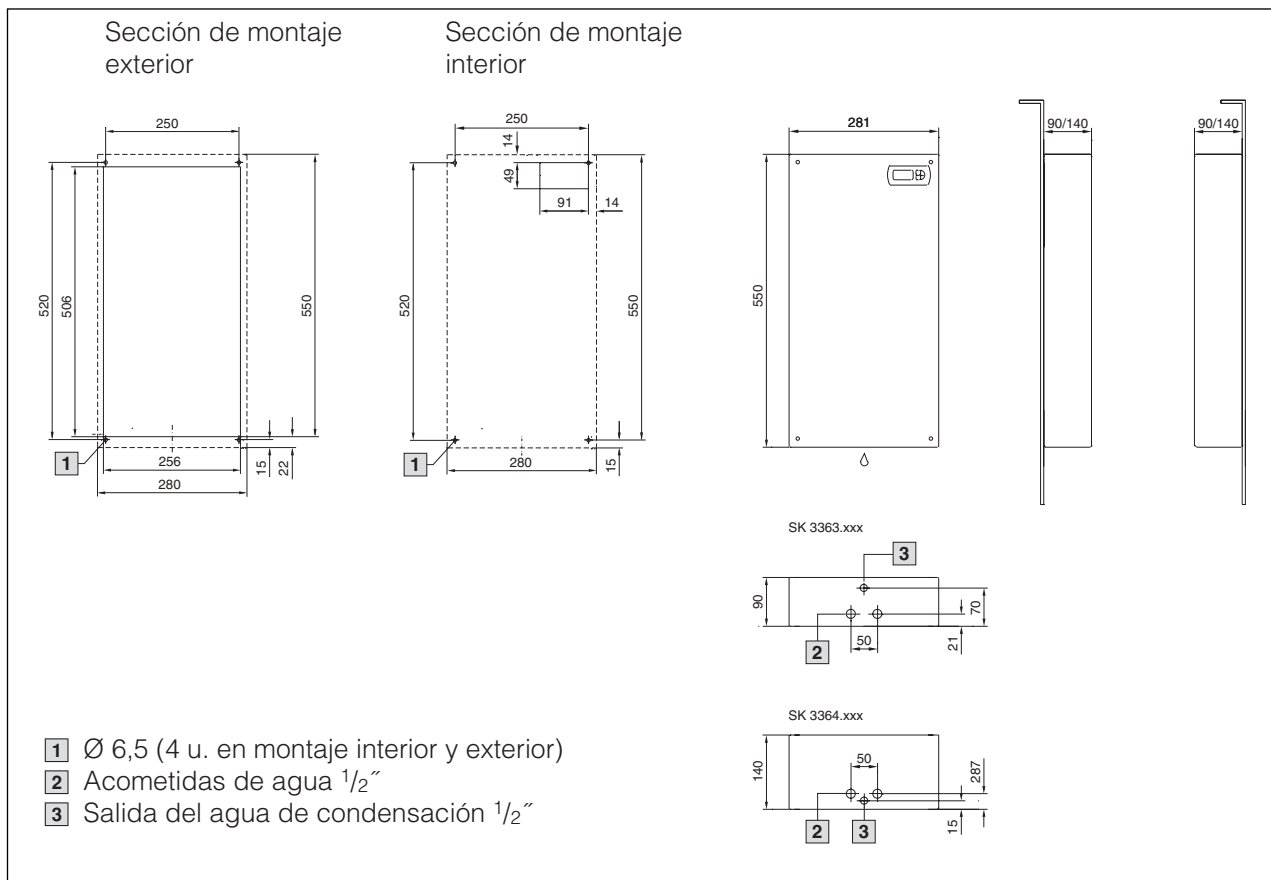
SK 3363.xxx/SK 3364.xxx montaje exterior
